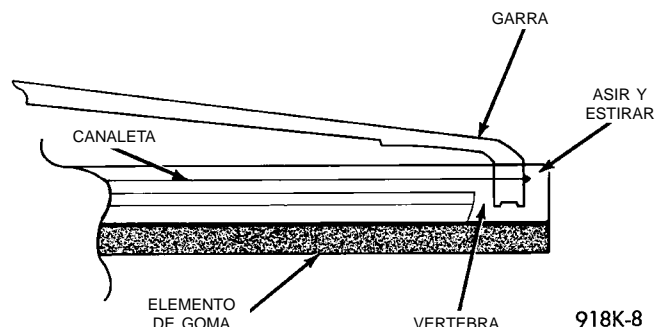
Desmontaje del elemento del limpiaparabrisas
